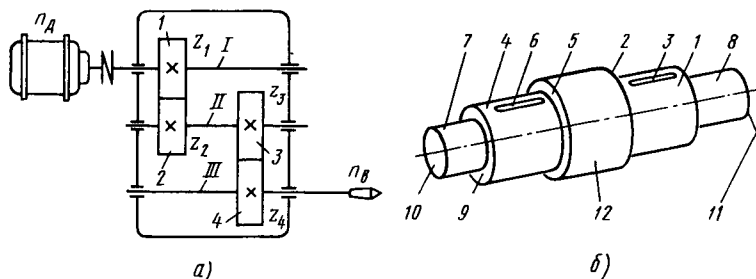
Кинематическая схема редуктора (а) и конструктивные формы вала II (б)
